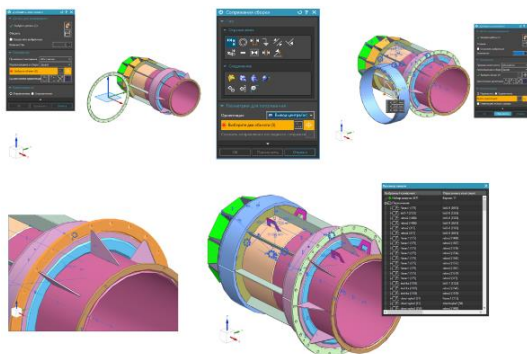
Сборка готовых деталей в области «Сопряжение сборки»
